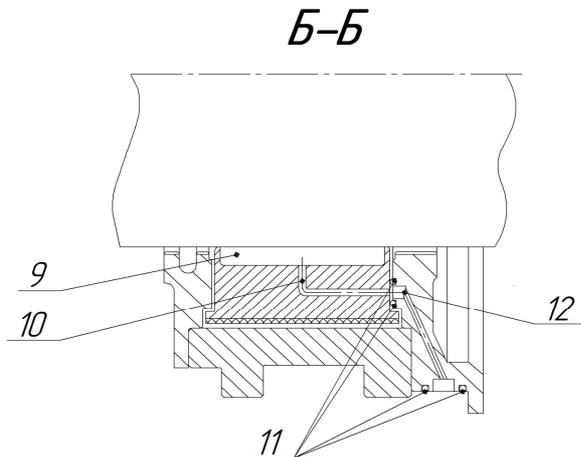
Схема подвода смазки в рабочую зону опорного подшипника:
